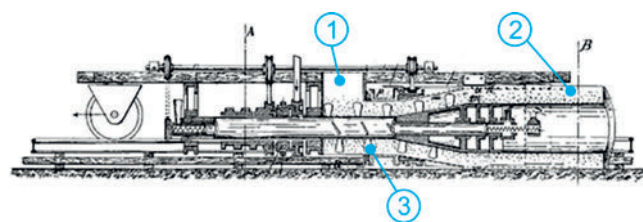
machine inventée par Gaiba pour la fabrication de tuyaux d'eau [22] ; (1) trémie de remplissage, (2) chambre de moulage, (3) axe de rotation avec des pales de pression
